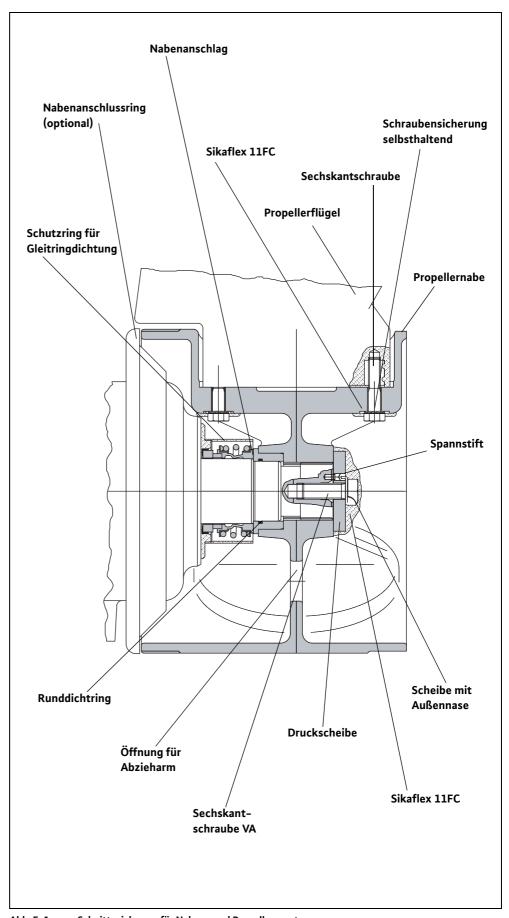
Schnittzeichnung für Naben- und Propellermontage
